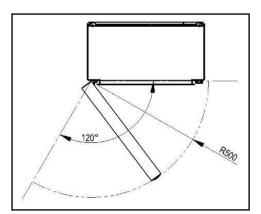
Dimensiones del Gabinete SAS - Apertura de puerta
